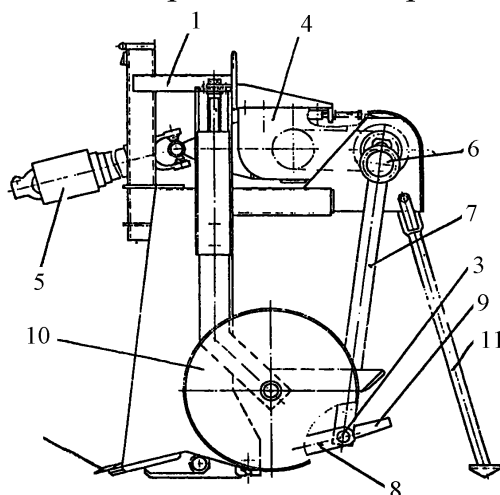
Выкопчная скоба НВС-1,5: 1 – рама; 2 – подрезной горизонтальный нож; 3 – ось; 4 – редуктор; 5 – карданный вал; 6 – эксцентрик; 7 – кулиса; 8 – плита; 9 – удлинитель; 10 – опорное колесо; 11 – ножка
